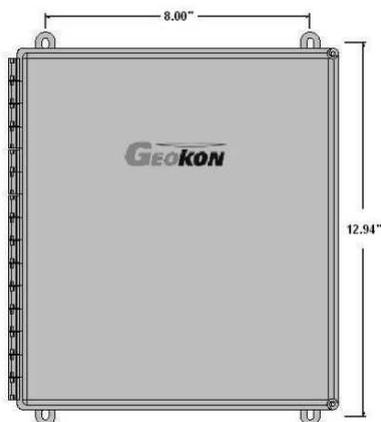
Dimensiones de montaje del gabinete del multiplexor
